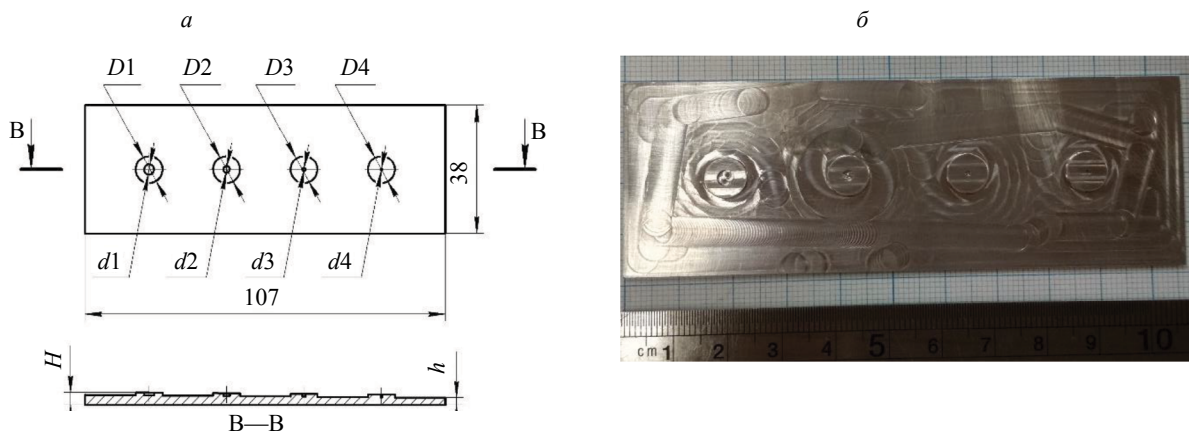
Образец настроечный с имитаторами дефектов типа непровар и имитаторами сварных зон: эскиз (а); общий вид (б).
